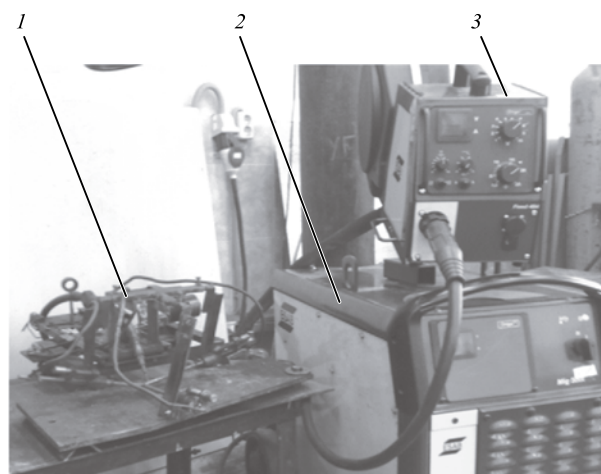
Установка и оборудование для наплавки порошковой проволокой с опережающей трехфазной дугой:
